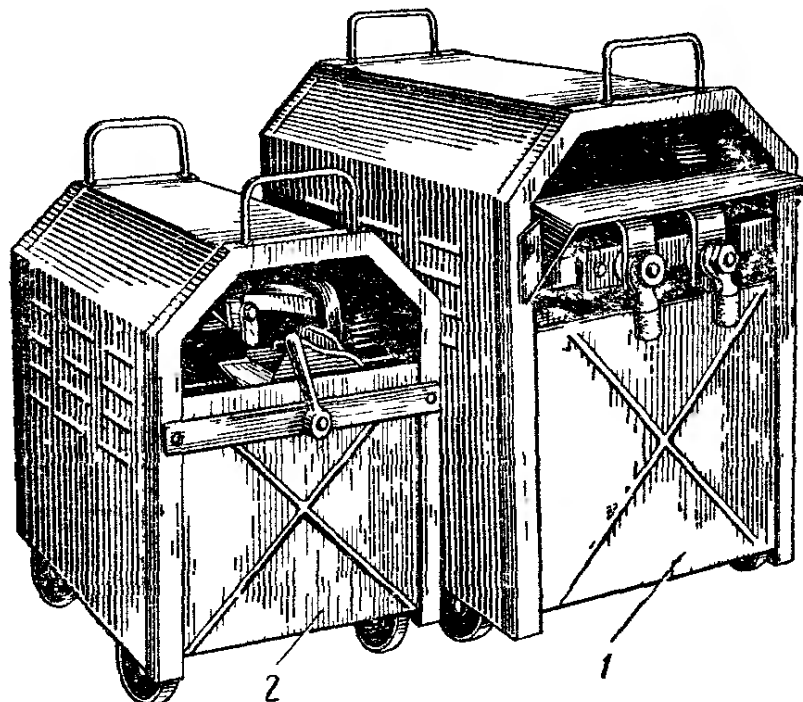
Сварочный трансформатор СТЭ-34 с регулятором.
